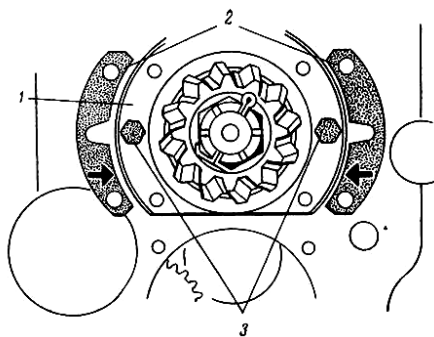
Регулировка осевого зазора в подшипниках вторичного вала: 1 - стакан вторичного вала, 2 - регулировочные прокладки; 3 - технологические болты
